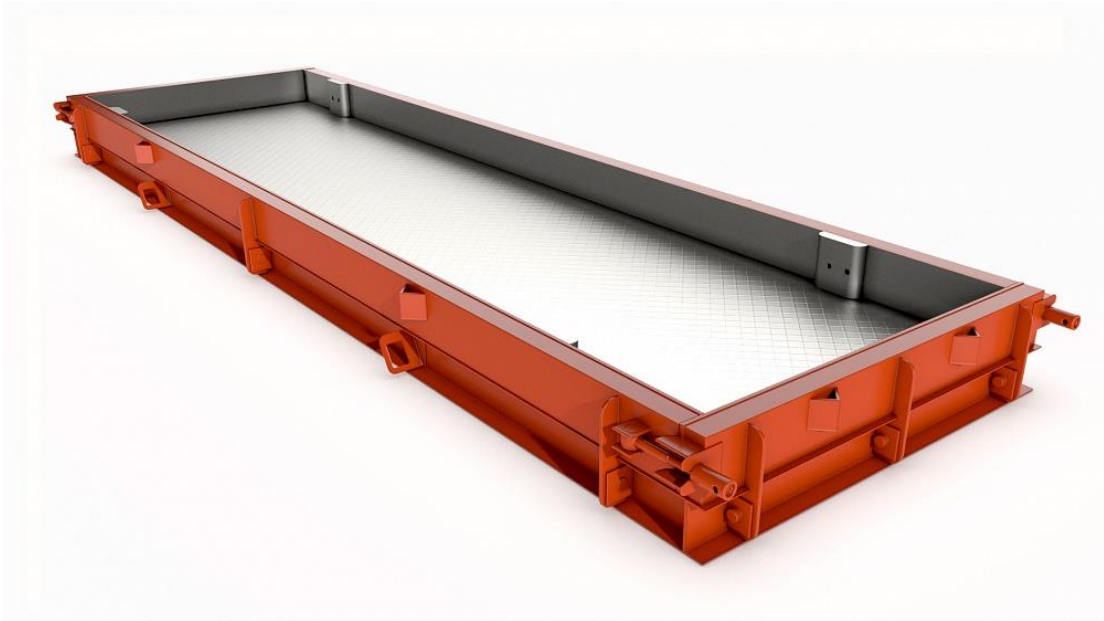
Загальний вигляд форми для плит, що формують «лицем до низу»
